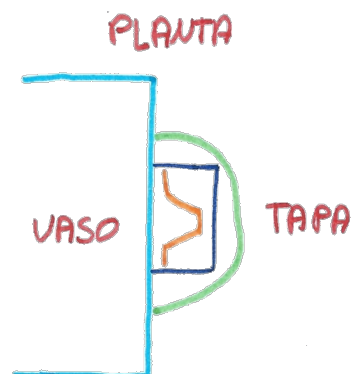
Columna media con un zigzag vertical (planta).
